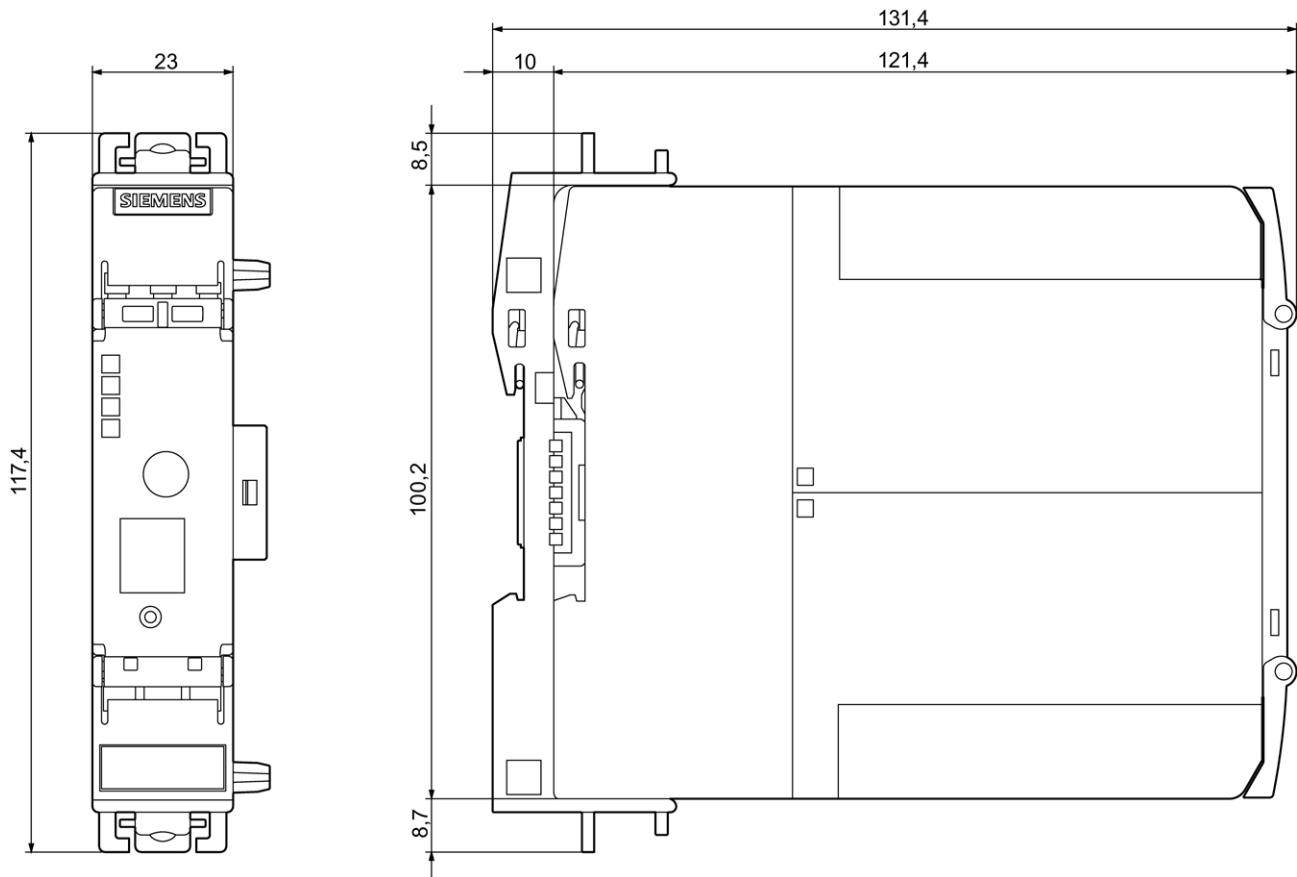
Gerät 3SK1 auf Geräteverbinder
